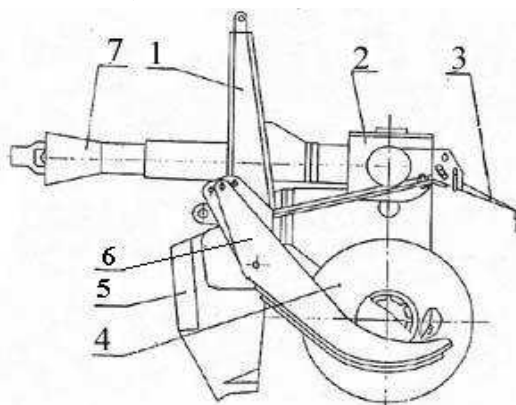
Фреза ФЛШ-1,2: 1 – рама с навеской; 2 – редуктор; 3 – кожух; 4 – шнек; 5 – нож; 6 – ограничительный полоз; 7 – карданная передача
